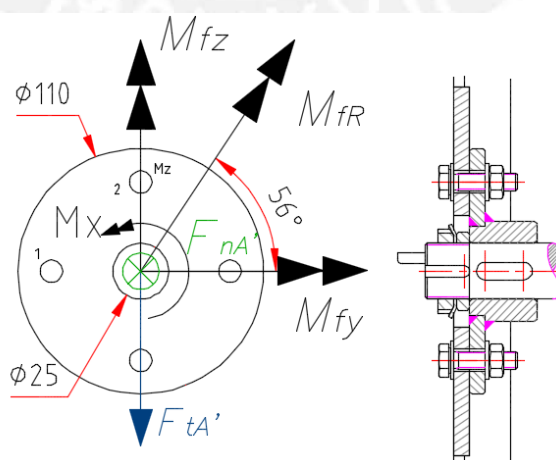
Vista frontal (izquierda) y vista de sección (derecha) de la unión atornillada arreglo de moldes - sistema de rotación.
